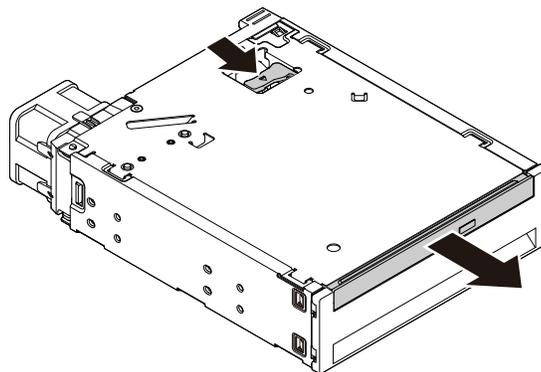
Ein flaches optisches Laufwerk aus dem Gehäuse entfernen
